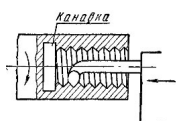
Канавка для выхода резьбового резца при нарезании внутренней резьбы
